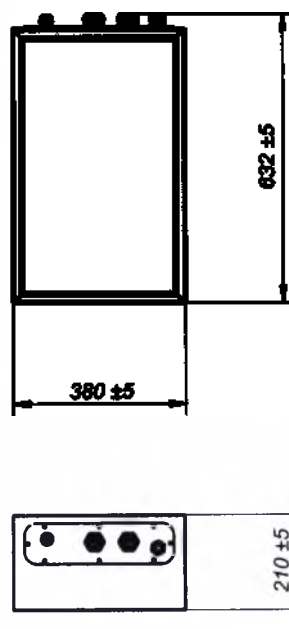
Габаритные размеры блока управления и контроля
